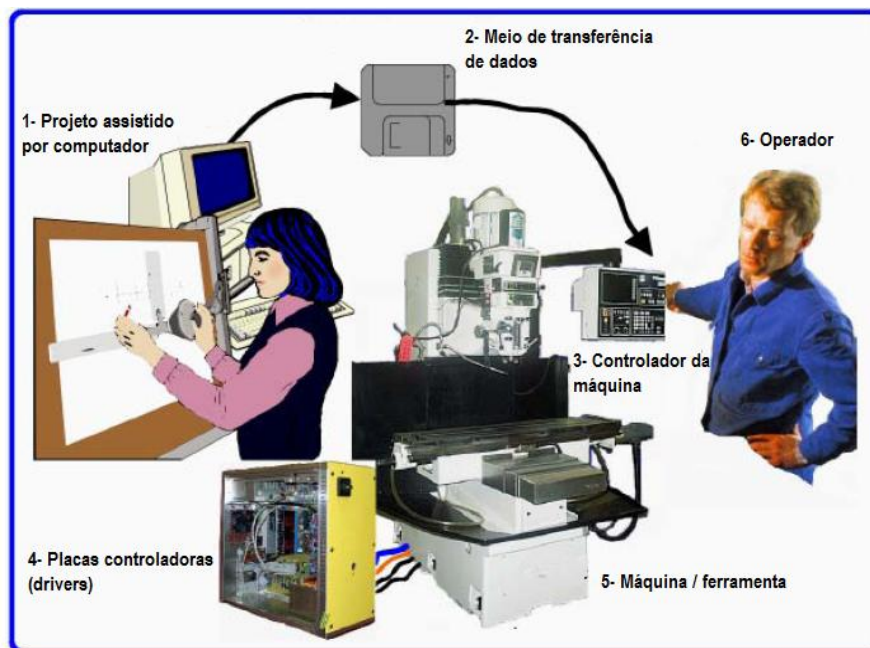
Componentes básicos de uma máquina CNC.
